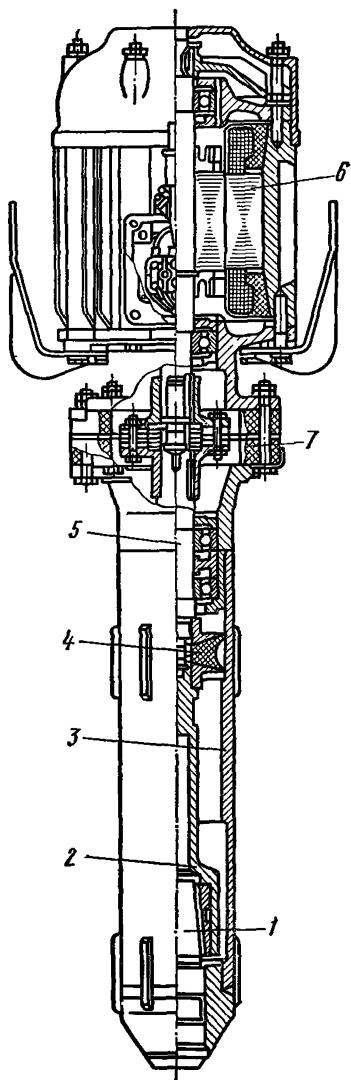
Подвесной глубинный вибратор ИВ-90:
